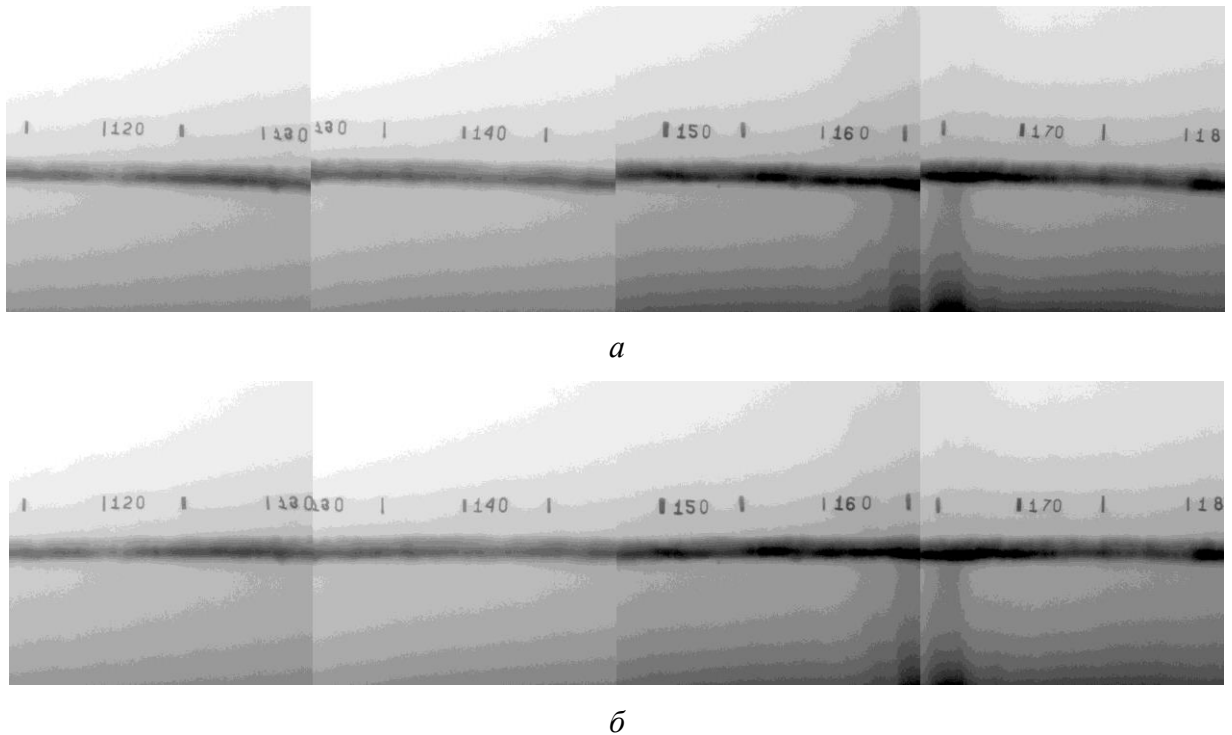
Негоризонтальная ориентация сварного шва: *a* – исходные кадры;
